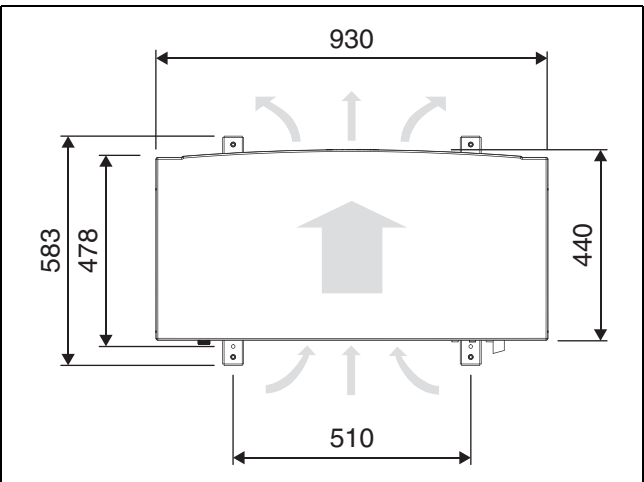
Dimensjoner til varmepumpetype 405-409, sett ovenfra
